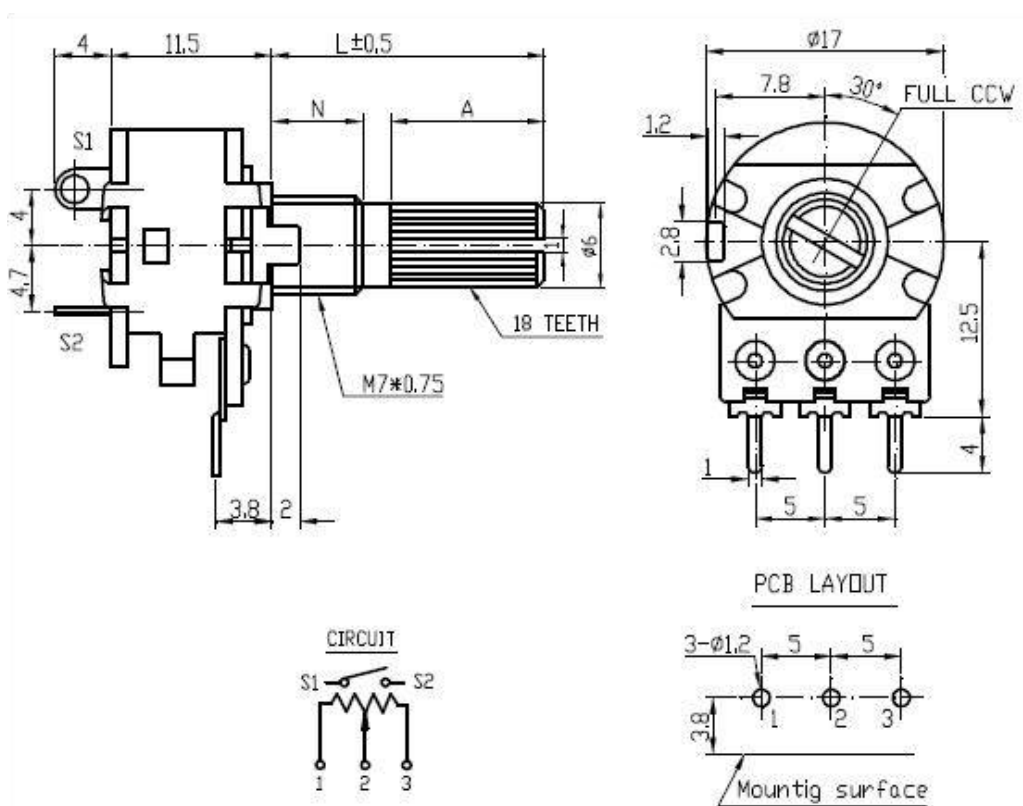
Зовнішній вигляд і розміри підстроювального резистора типу S16KN1-B – R10, R20, R22, R24.
